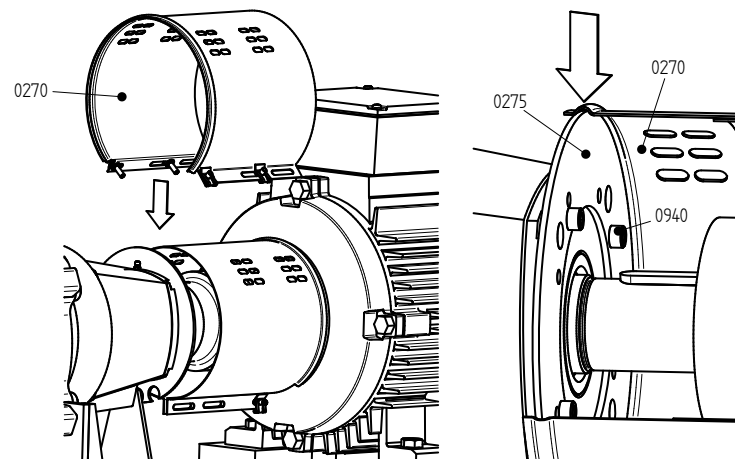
Montieren der Haube auf der Pumpenseite.
